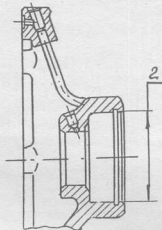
Корпус подшипника гидромукфы с трубкой в сборе
